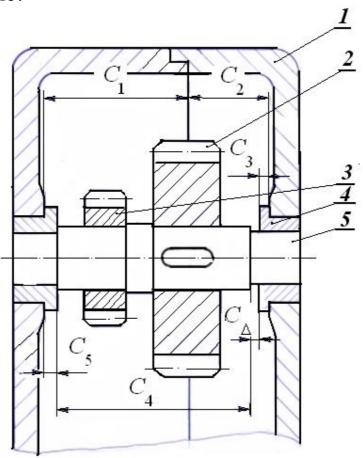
Общий вид редуктора: 1 – корпус; 2, 3 –зубчатое колесо; 4 – подшипник скольжения; 5 – вал
